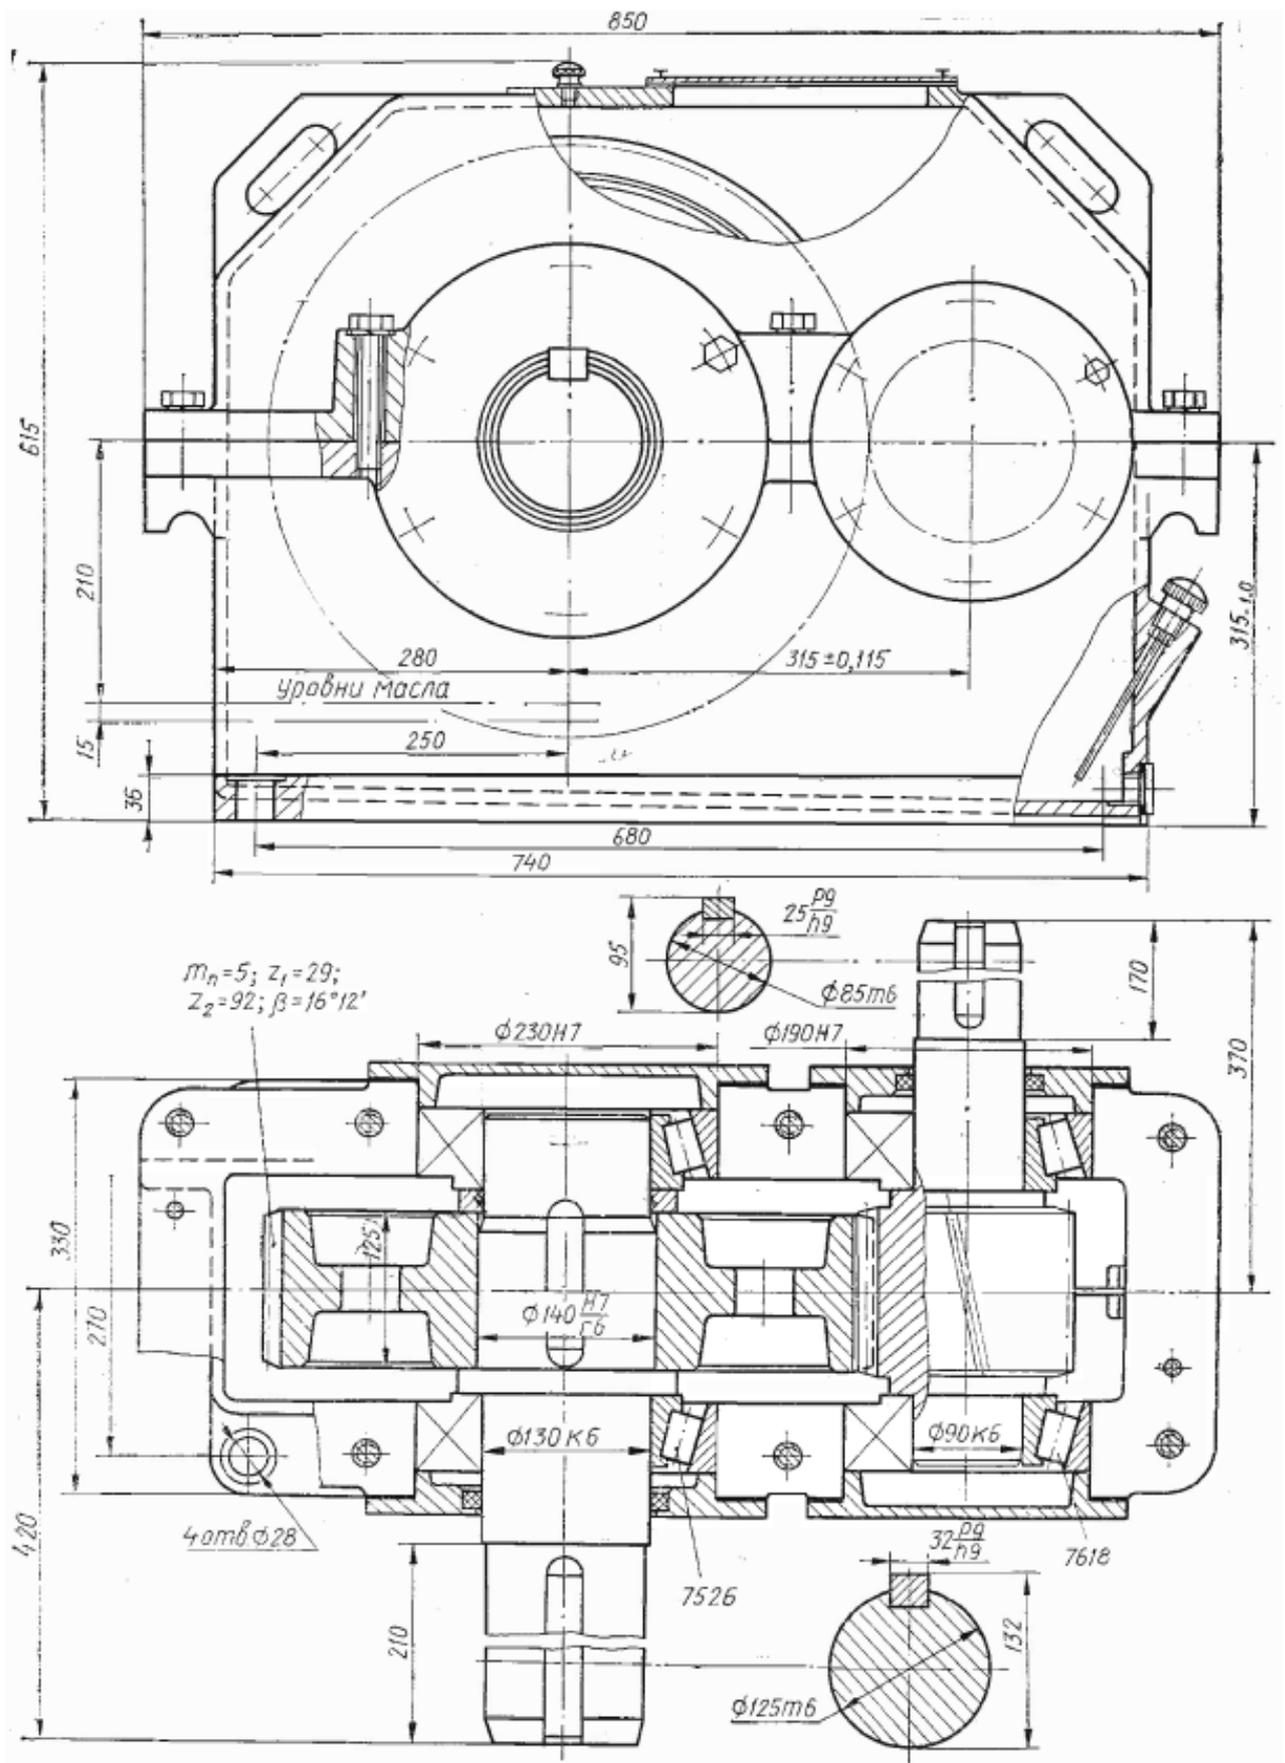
Редуктор с накладными крышками и коническими роликоподшипниками
